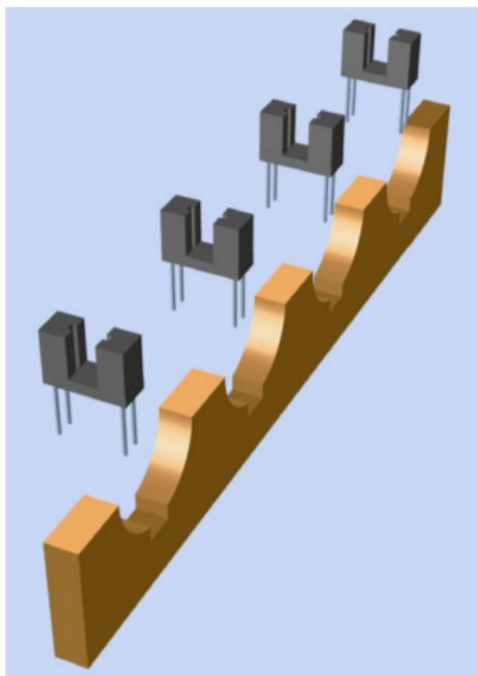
Première étape d'assemblage des capteurs dans un boîtier.
